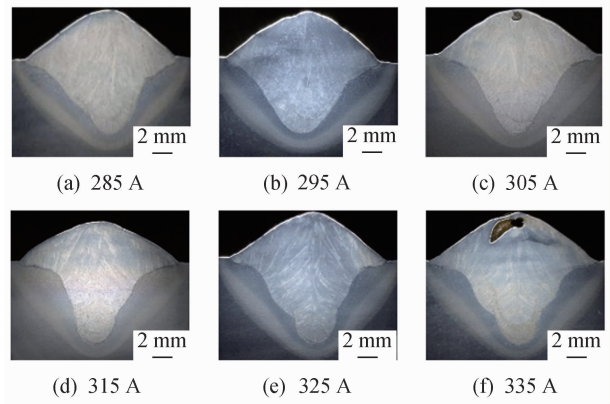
深熔 GMAW 不同焊接电流下的接头截面形貌
